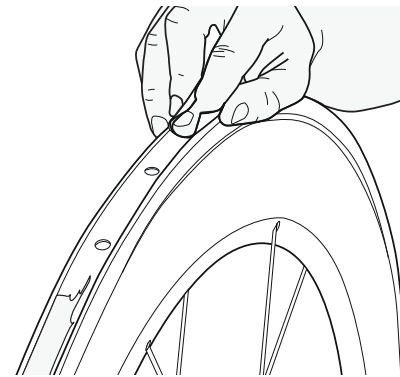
Felgenbett leicht anrauen. Mit etwas Azeton und einem Lappen reinigen.
